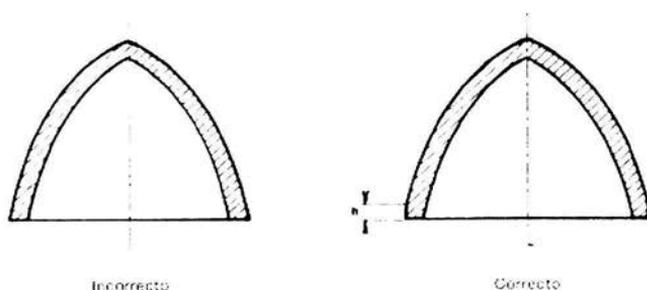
Sección perimetral cilíndrica, para facilitar el rebabeo.
